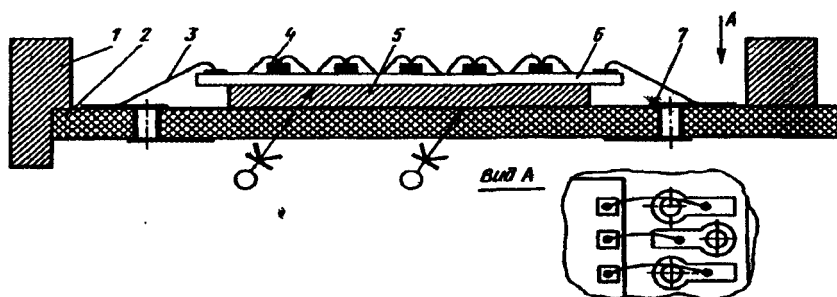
Схема установки и монтажа бескорпусных МСБ на металлической рамке: 7 — ребро рамки; 2 — печатная плата; 3 — соединительный проводник; 4 — бескорпусная ИС; 5 — планка; 6 — подложка; 7 — металлизированное отверстие
